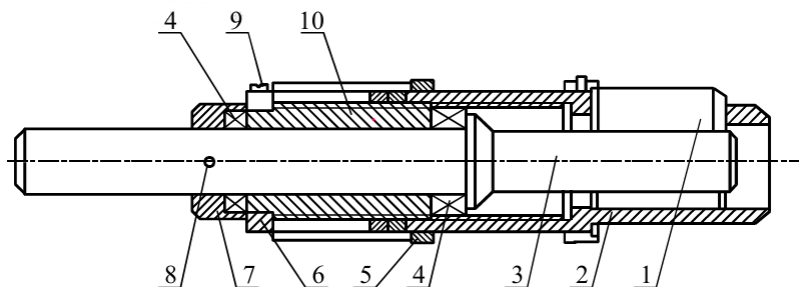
Розкатка роликова: 1 – ролик; 2 – корпус; 3 – стрижень з конусом; 4 – шарикопідшипники упорні; 5 – гайка; 6 – кільце; 7 – упорне кільце; 8, 9 – штифти; 10 – гвинт регулювальний
